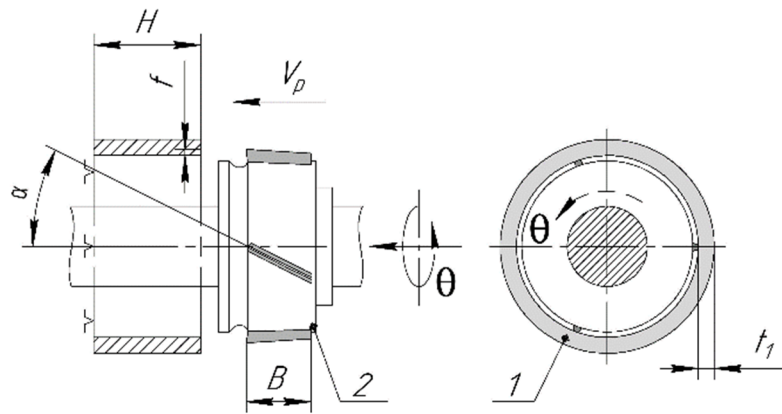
Схема обработки внутренних винтовых канавок в тонкостенных деталях протяжкой, реализующей скрытую кинематическую связь: 1 – обрабатываемая заготовка, 2 – участка заготовки, мм; B – ширина зуба протяжки, мм; V_p – скорость резания, м/мин.; θ – угол поворота инструмента при его поступательном движении, град. t_1 – толщина стенки заготовки, мм; f – величина подъема на зуб (слоя срезаемого одним рядом режущих зубьев), мм; α – угол наклона зуба инструмента (номинальный угол наклона спирали), град.
